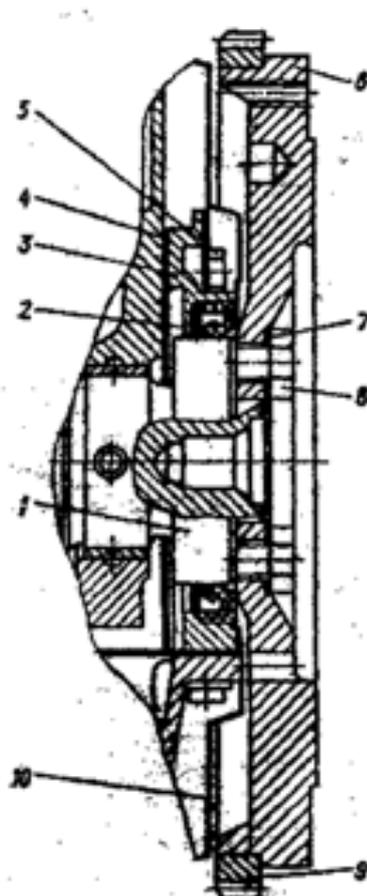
Задний конец коленчатого вала: 1 - вал коленчатый; 2 - манжета коленчатого вала задняя; 3 - держатель манжеты; 4 - прокладка держателя; 5 - болт; 6 - маховик; 7 - шайба болтов крепления маховика; 8 - болт крепления маховика; 9 - обод зубчатый маховика; 10 - кожух защитный
